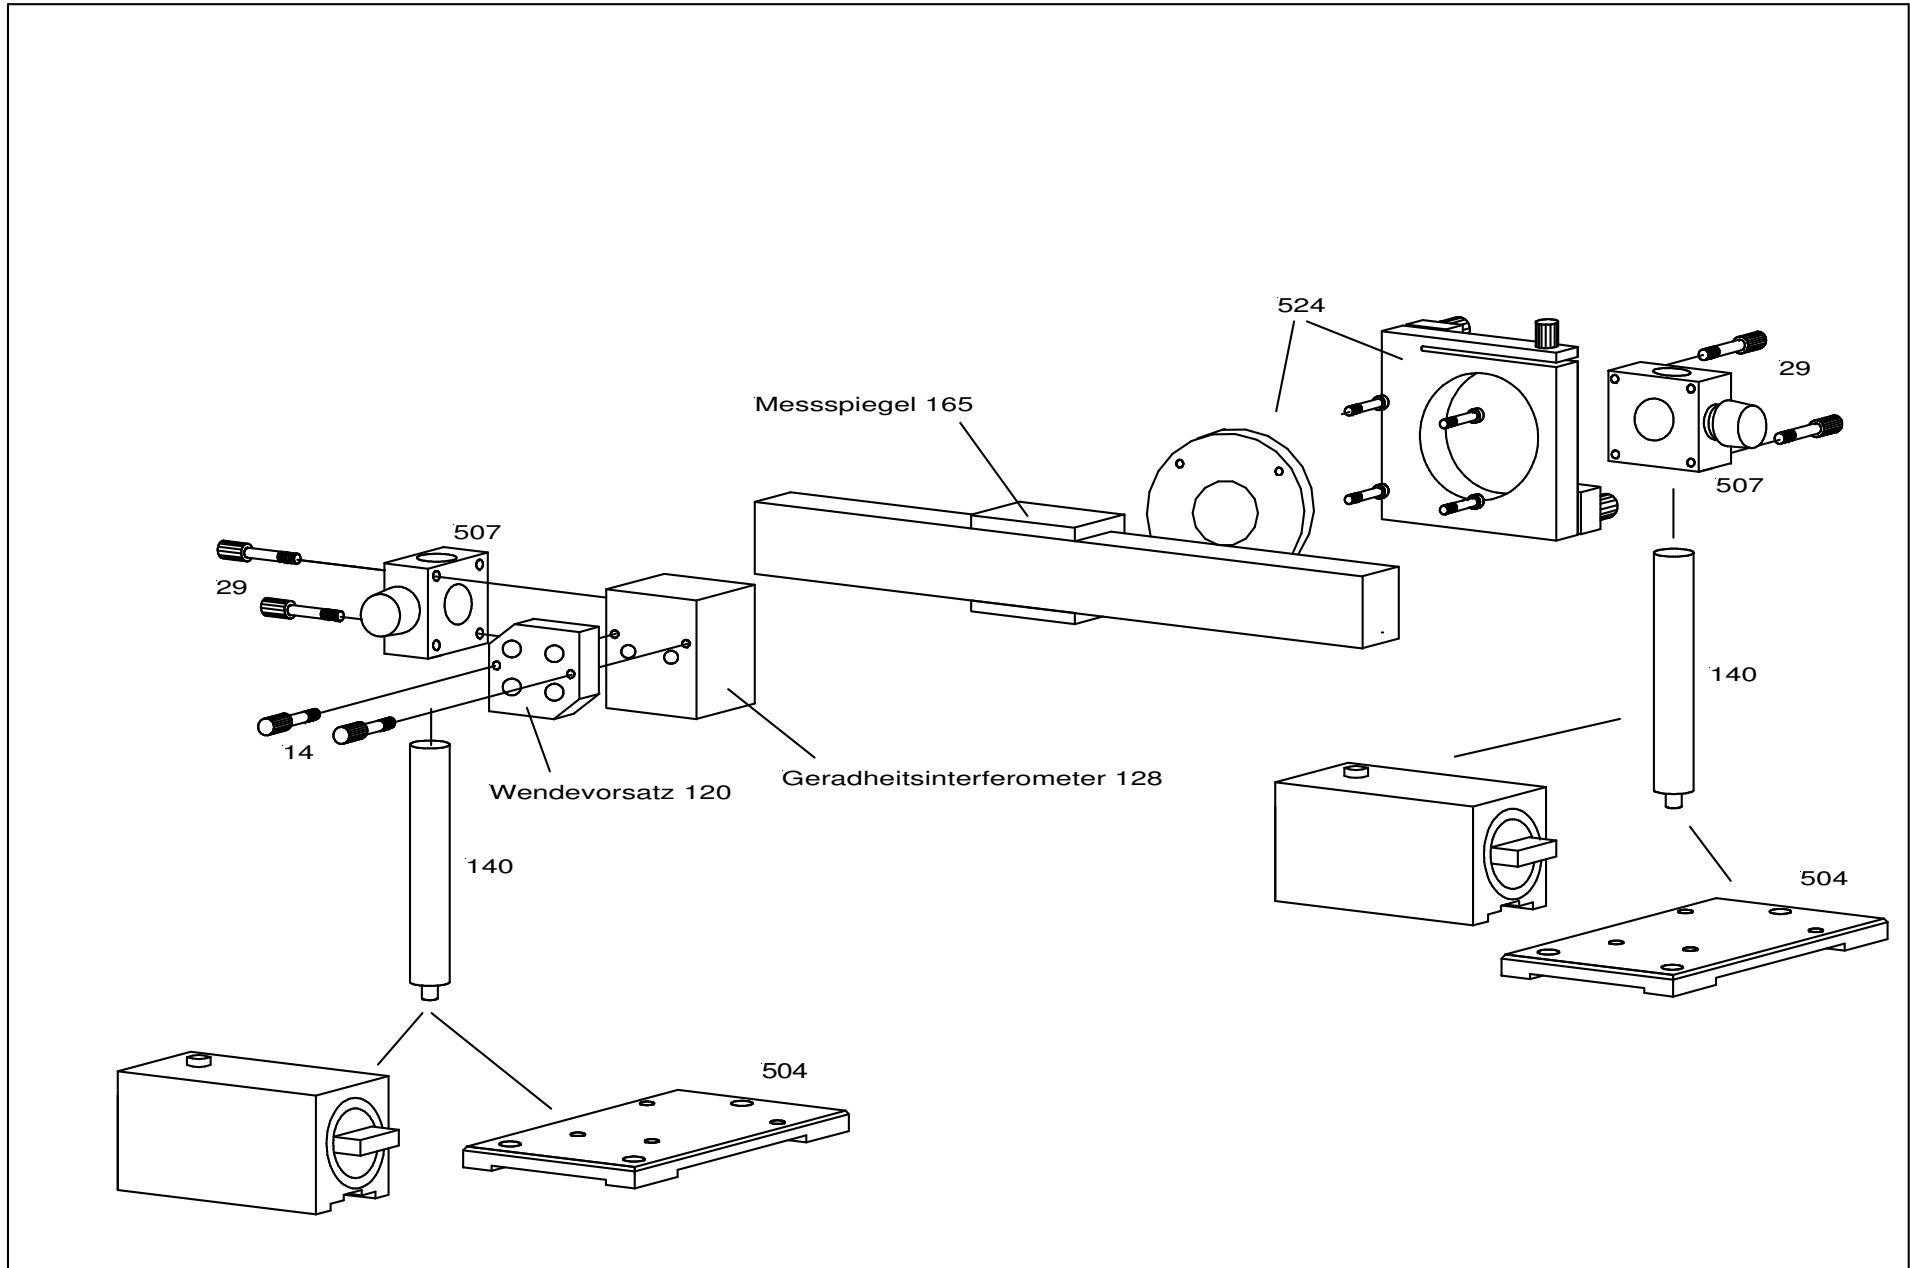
Rollwinkelmessung mit Geradheitsinterferometer horizontaler Aufbau
